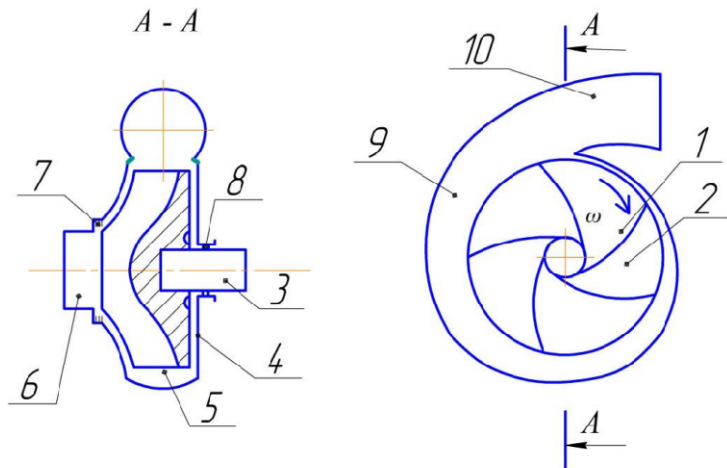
Схема центробежного насоса. 1 – рабочее колесо; 2 – лопасть; 3 – вал; 4 – корпус; 5 – рабочая камера; 6 – всасывающий патрубок; 7, 8 – уплотнение; 9 – спиральный отвод; 10 – напорный патрубок
